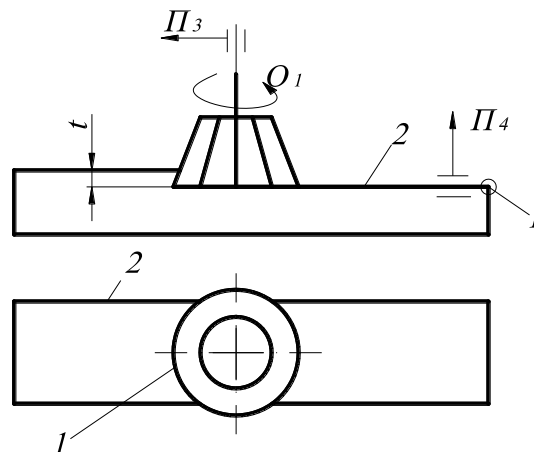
Схема фрезерування площини торцевою фрезою
